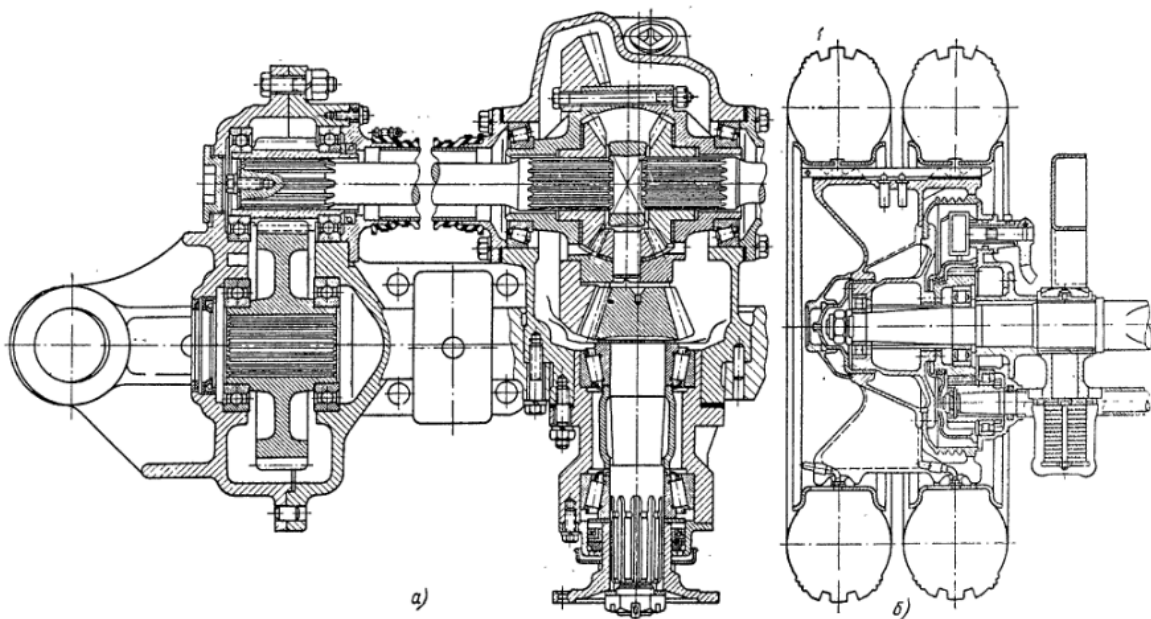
Бортовая передача (а) и колесный редуктор(б)
